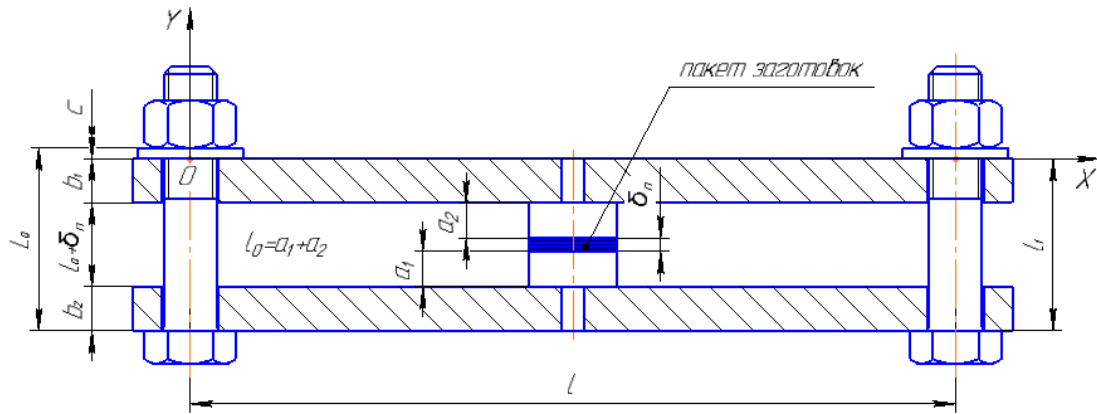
Розрахункова схема пристрою для зварювання при наявності пакету зразків
